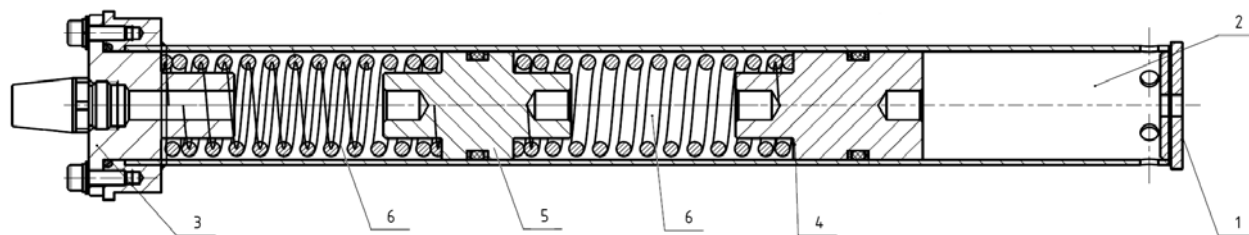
Компенсатор расширения объема РЖ: 1 – задняя крышка; 2 – корпус; 3 – передняя крышка в сборе; 4,5 – поршень; 6 – пружина
